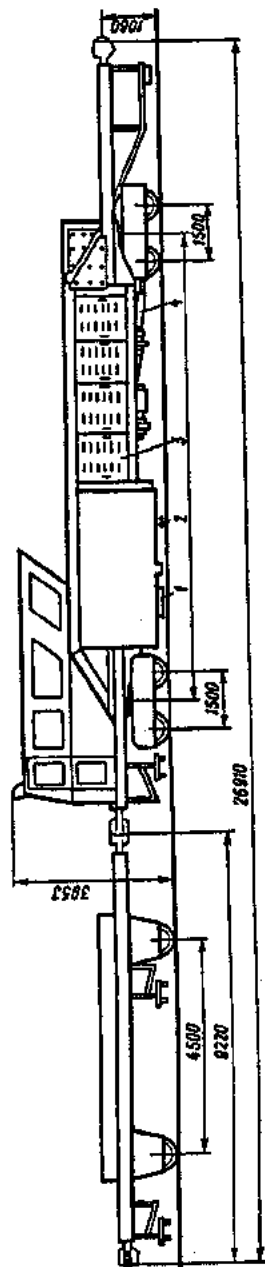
Рихтовочная машина Р-2000: 1 — уплотнитель балласта; 2 — рихтовочное устройство; 3 — измерительная установка; 4 — силовая передача
